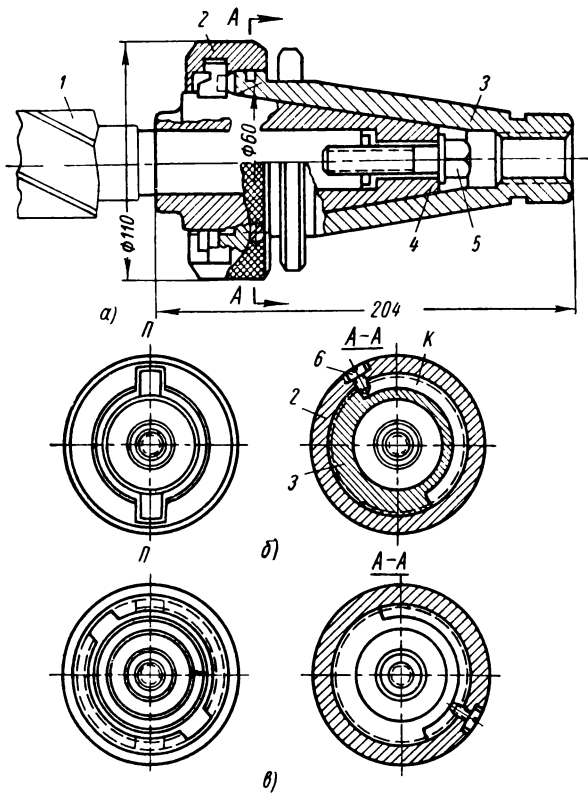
Быстродействующий патрон для закрепления концевых фрез конструкции новаторов Ленинградского Кировского завода
